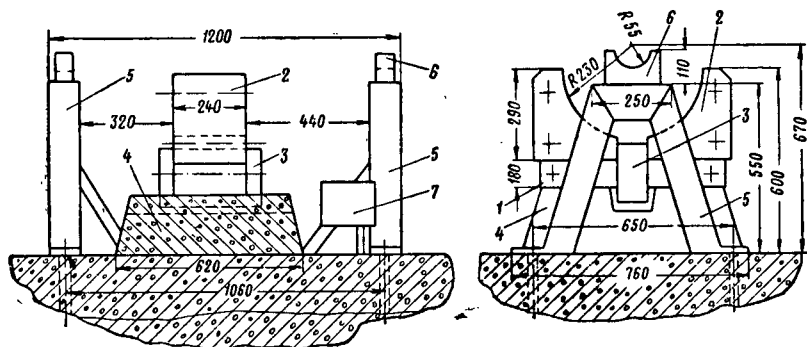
Установка для проверки якорей тяговых двигателей ДК-103 и ДПИ-150 на витковое замыкание:
